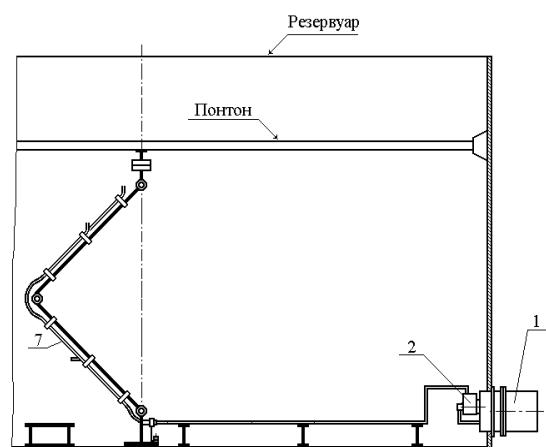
Пробоотборник стационарный для послойного отбора проб из резервуара с понтонами
